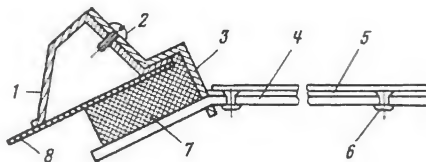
Установка столика: 1 — окантовка; 2 — саморез; 3 — серьга; 4 — опора; 5 — столик; 6 — заклепка; 7 — обивка передней панели; 8 — дно вещевого ящика.
